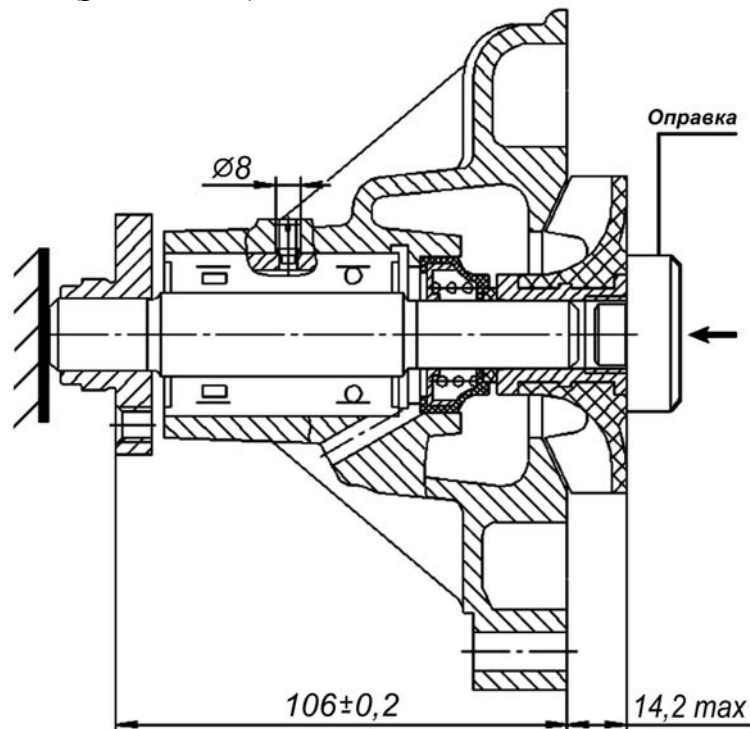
Напрессовка ступицы и крыльчатки насоса
